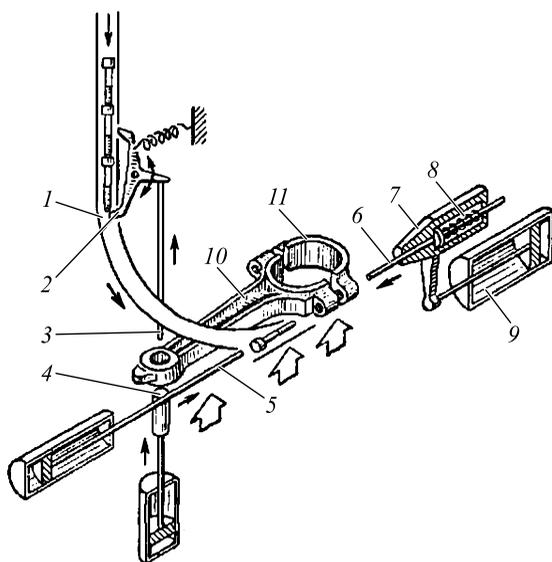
Схема автоматического устройства для запрессовки болтов в шатуны
